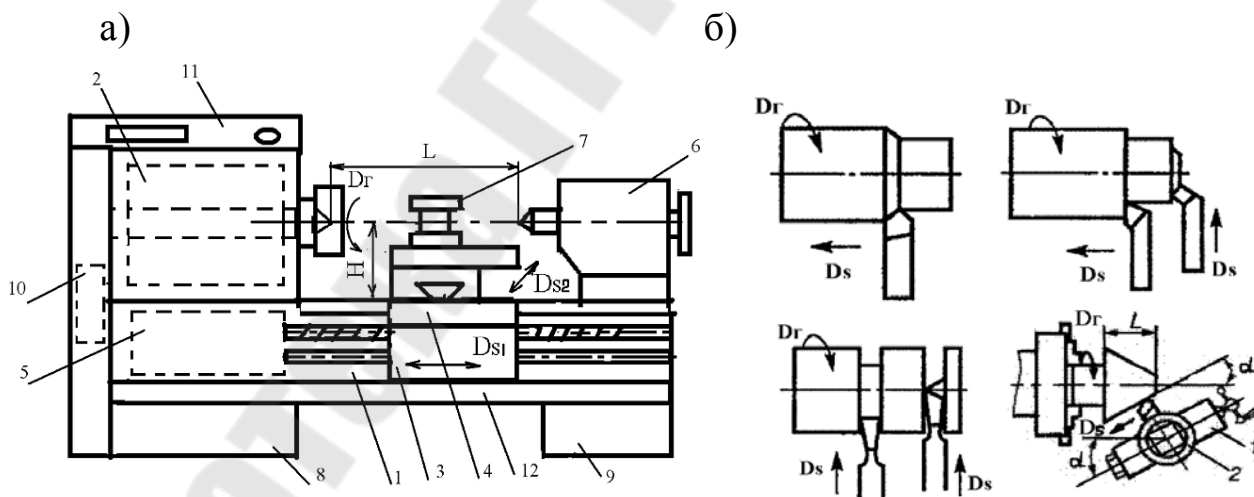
Компоновка токарно-винторезного станка (а) и схемы обработки (б)
